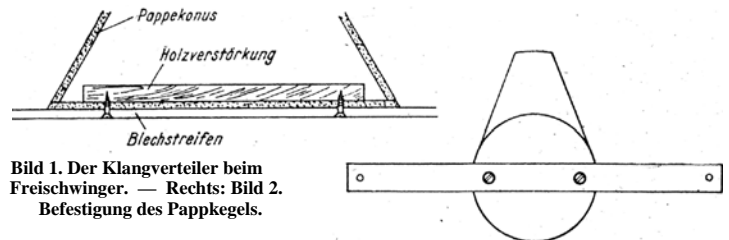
Der Klangverteiler beim Freischwinger. — Rechts: Bild 2. Befestigung des Pappekegels.
